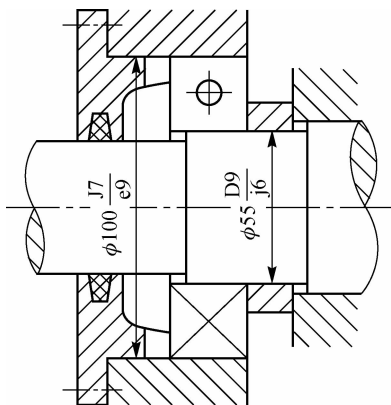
轴承盖与孔、轴承挡圈与轴的配合
